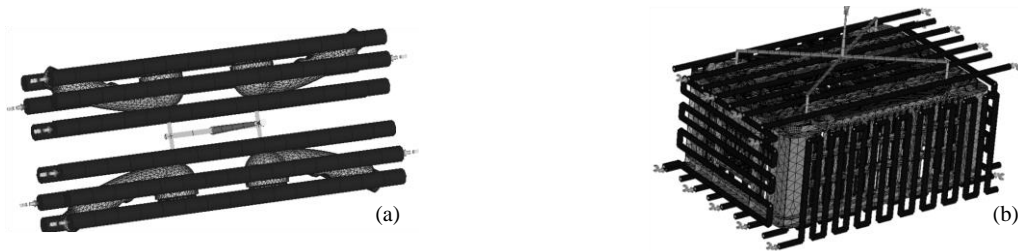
Diseño de Moldes Final : (a) Ducha y (b)Cesta.
